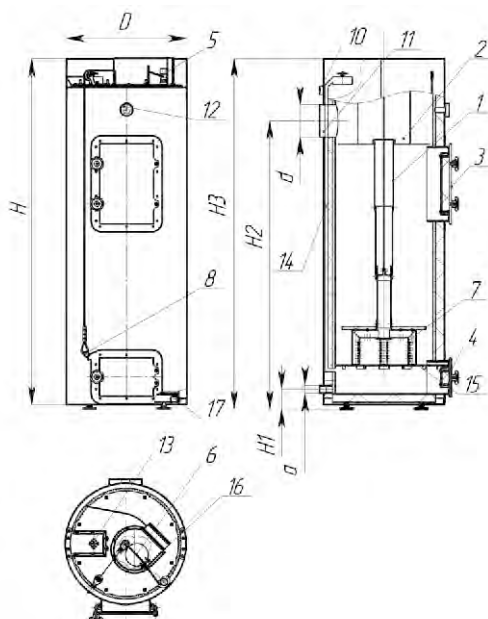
Габаритные и присоединительные размеры универсальной версии Comfort-XXG (1 – телескопическая труба подачи воздуха, 2 – камера подогрева воздуха, 3 – проем для загрузки дров, 4 – проем для удаления золы, 5 – терморегулятор, 6 – устройство для регулирования подачи воздуха, 7 – распределитель воздуха, 8 – трос, 10 – патрубок подачи воды, 11 – дымоход для отвода дымовых газов, 12 – термоманометр, 13 – регулятор подачи воздуха под колосниковую решётку, 14 – воздуховод, 15 – колосниковая решётка, 16 – воздушный короб с вентилятором).
